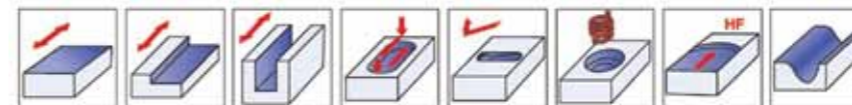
Типы операций, выполняемых фрезой CHASE-4-MILL
